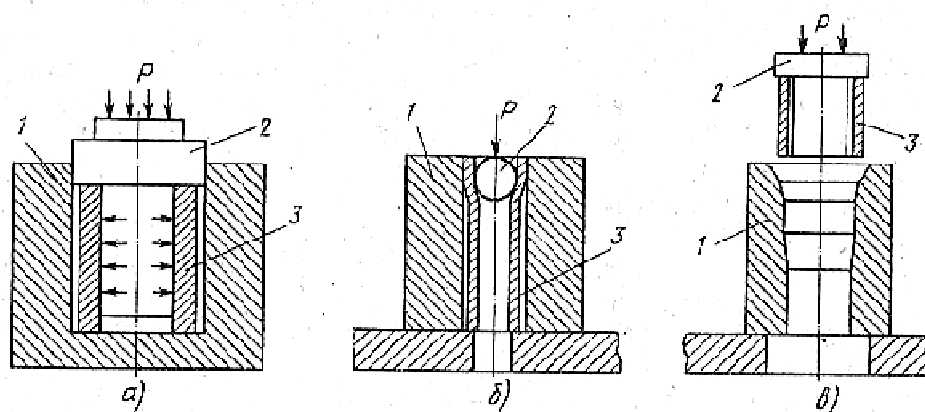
Способы ремонта деталей пластической деформацией:
